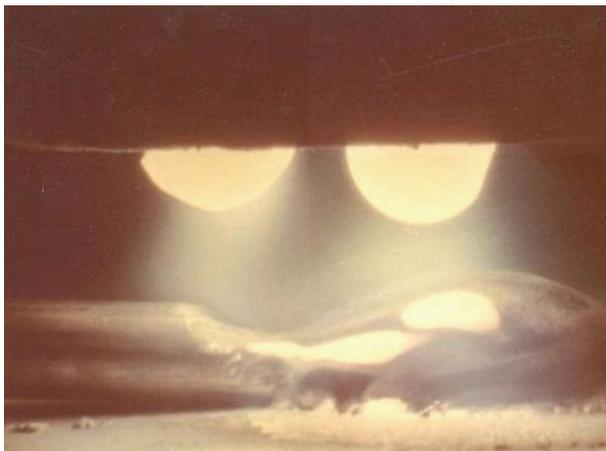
Процесс наплавки поверхности изделия трехфазной дугой
